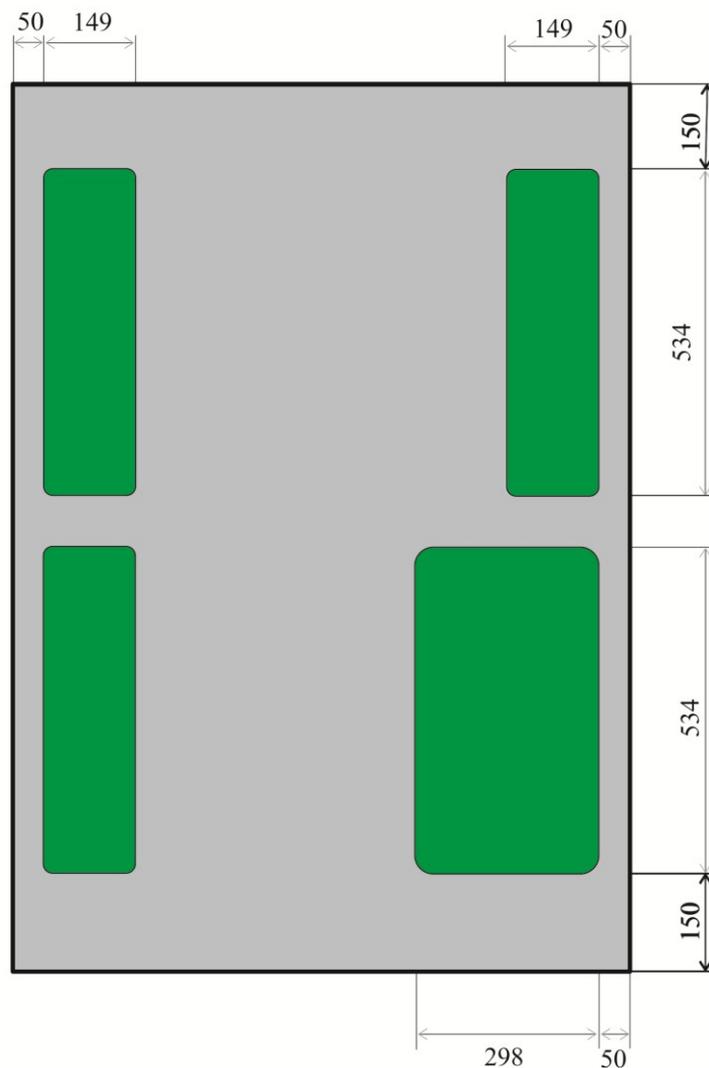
Kabeldurchführungen Seitenteile links mit Druckentlüftungsklappe
